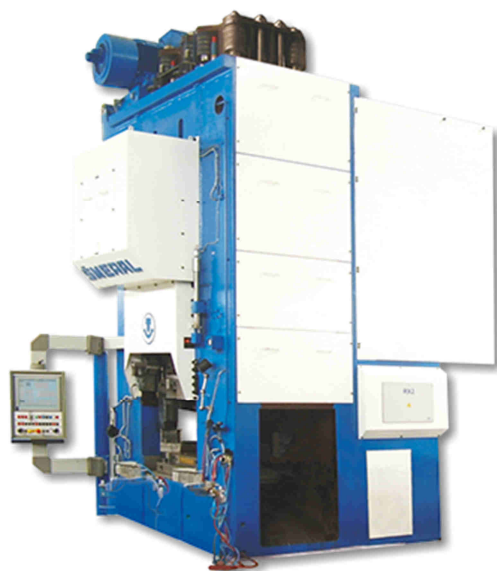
Pneumaticko-hydraulický buchar KHZ 4A [14]
